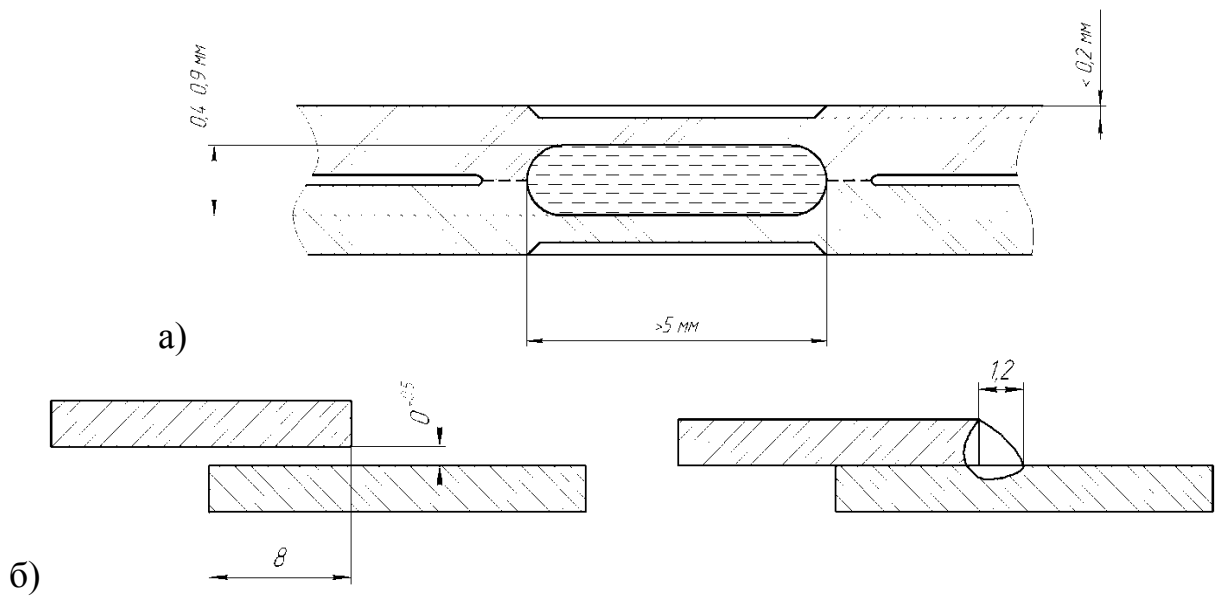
Требуемые геометрические размеры сварной точки (а) и сварного шва (б)
